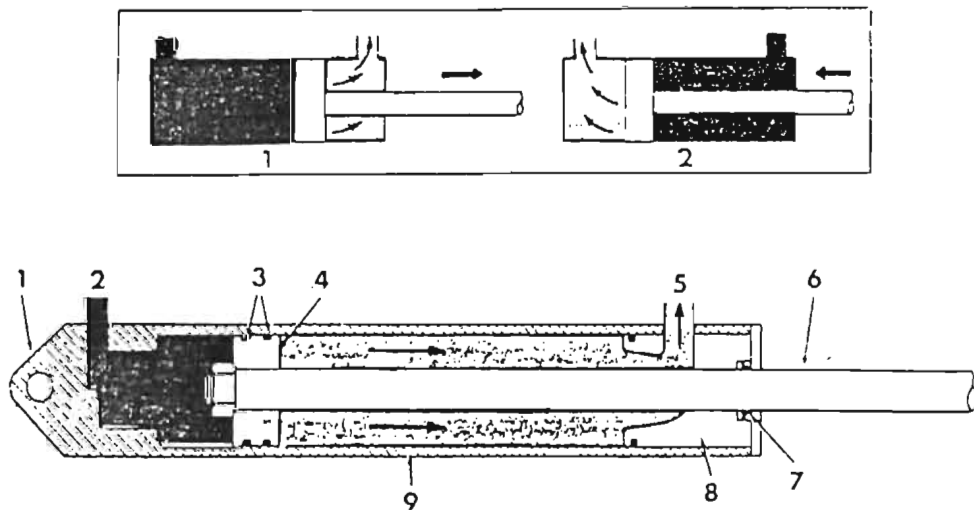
Partes y funcionamiento del cilindro de doble efecto. 1. Charnela; 2. Boca de aceite; 3. Juntas de pistón; 4. Pistón; 5. Boca de aceite; 6. Biela del pistón; 7. Juntas de biela; 8. Extremo desmontable; 9. Cilindro.
